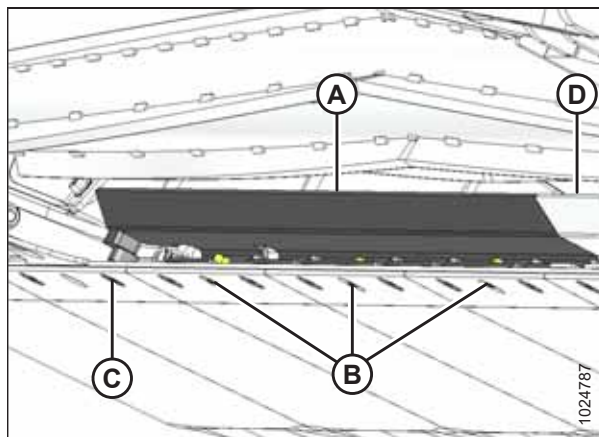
Déflecteur gauche – Derrière la barre de coupe
